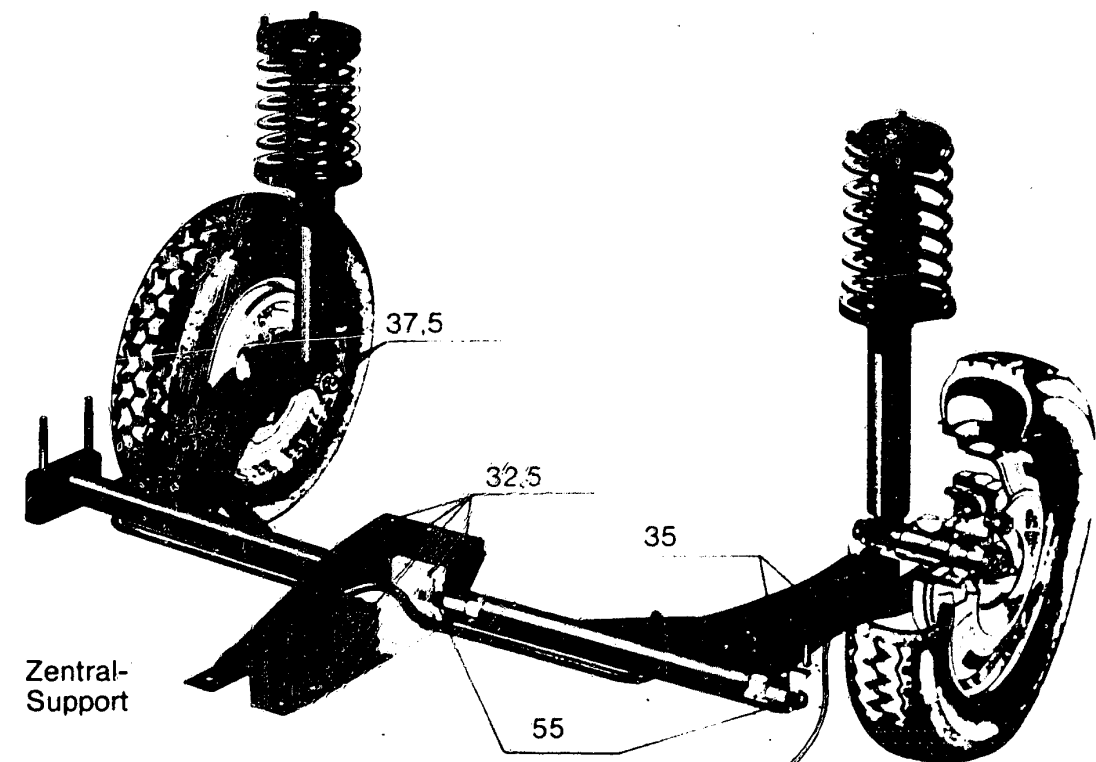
Hinterradaufhängung mit Anzugsdrehmomenten (Nm) für die Achsbefestigungsschrauben.
